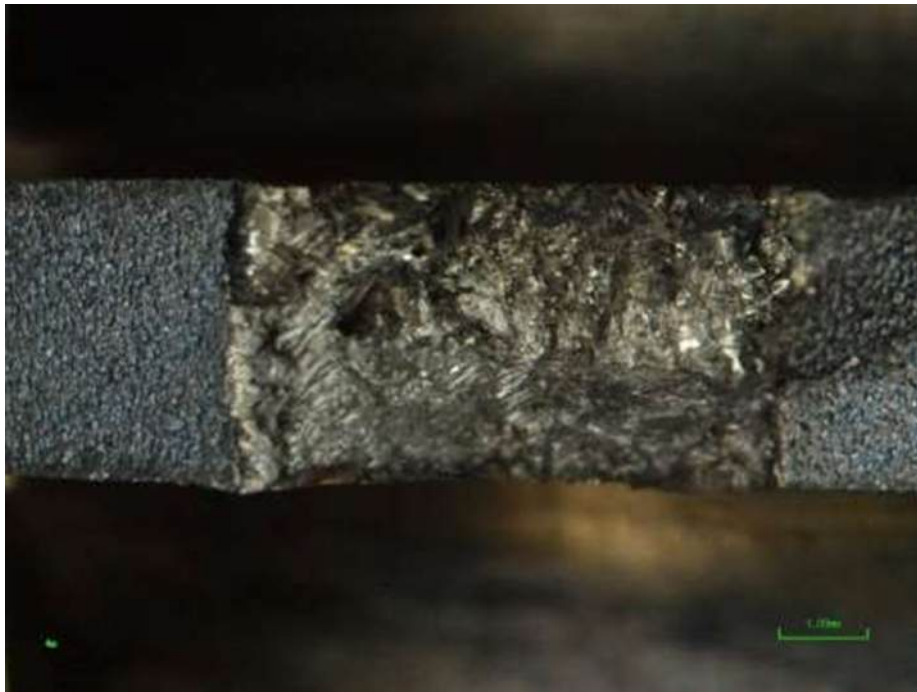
Общий вид трещины излома образца после ЛУО
